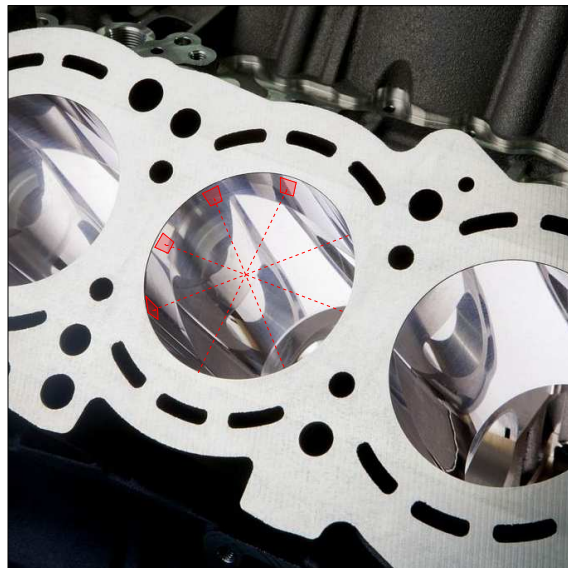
Foto eines fertig bearbeiteten ZKG, in dem acht verschiedene Winkelpositionen in einer Zylinderbohrung rot markiert sind. Die magnetische Sensorik wurde an vierzylinderigen ZKG an insgesamt 32 Messpositionen erprobt (vier Zylinderbohrungen à acht Winkelpositionen).
